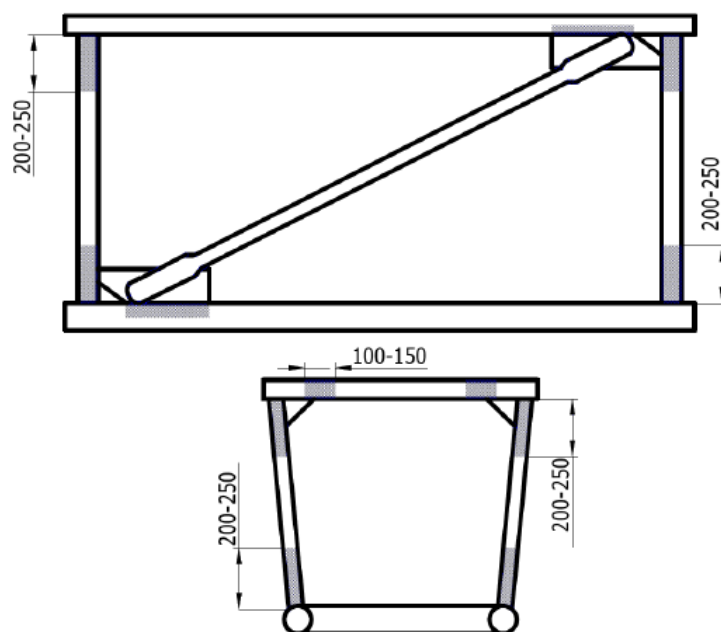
Зоны контроля рамы подвески компрессорного агрегата МАБ-2
